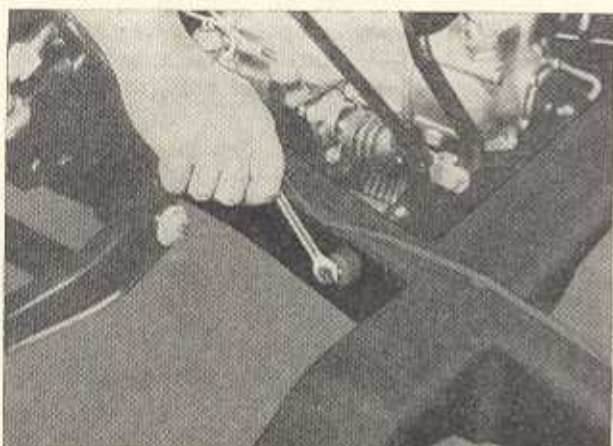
Heraus-schrauben der Sechskantschraube M 6 an der Fußhebelwelle
